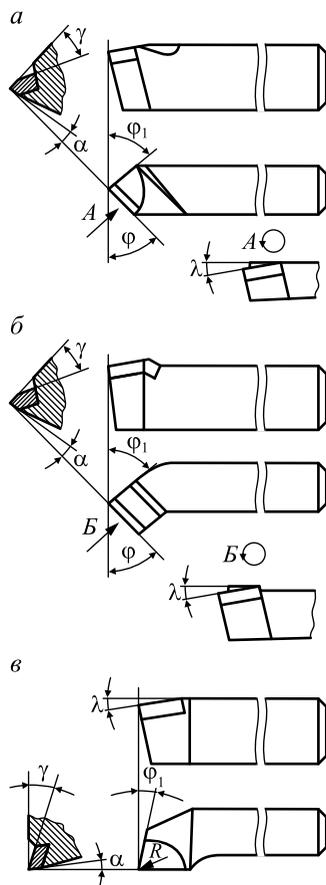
Прходные резцы: а — прямой; б — отогнутый; в — упорный; γ , α , λ , ϕ , ϕ_1 — углы резца; R — радиус закругления режущей кромки
